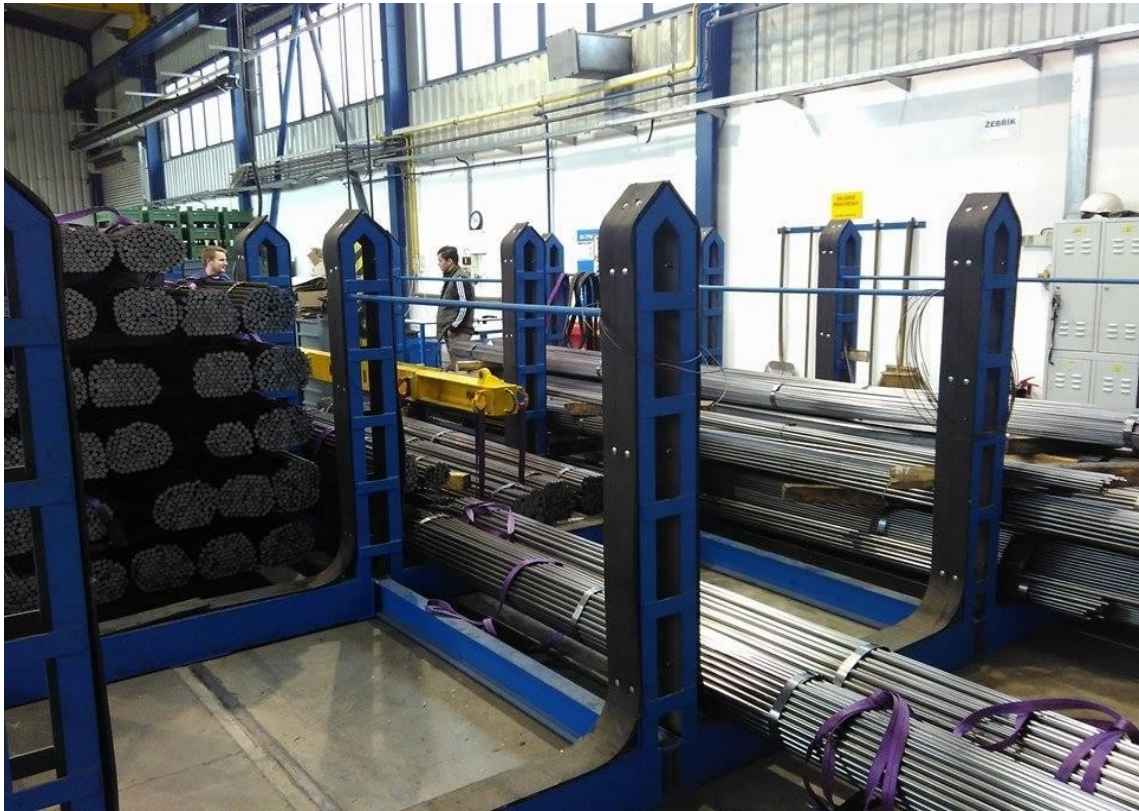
Layout haly – současný stav (vlastní zpracování)
